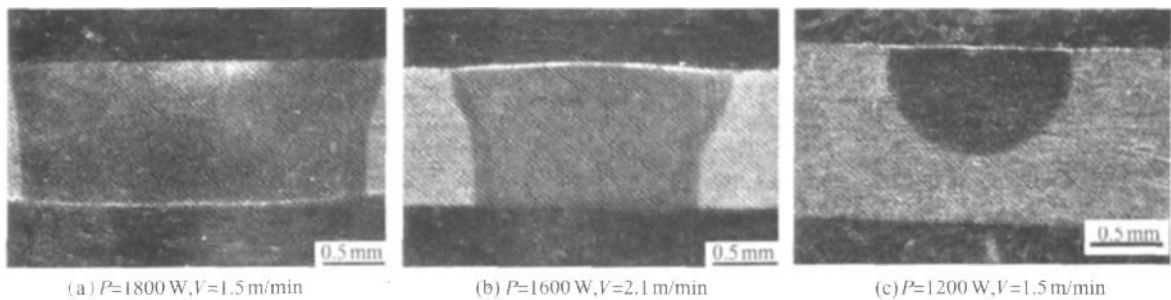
TiNiNb 合金激光焊接焊缝断面形貌
